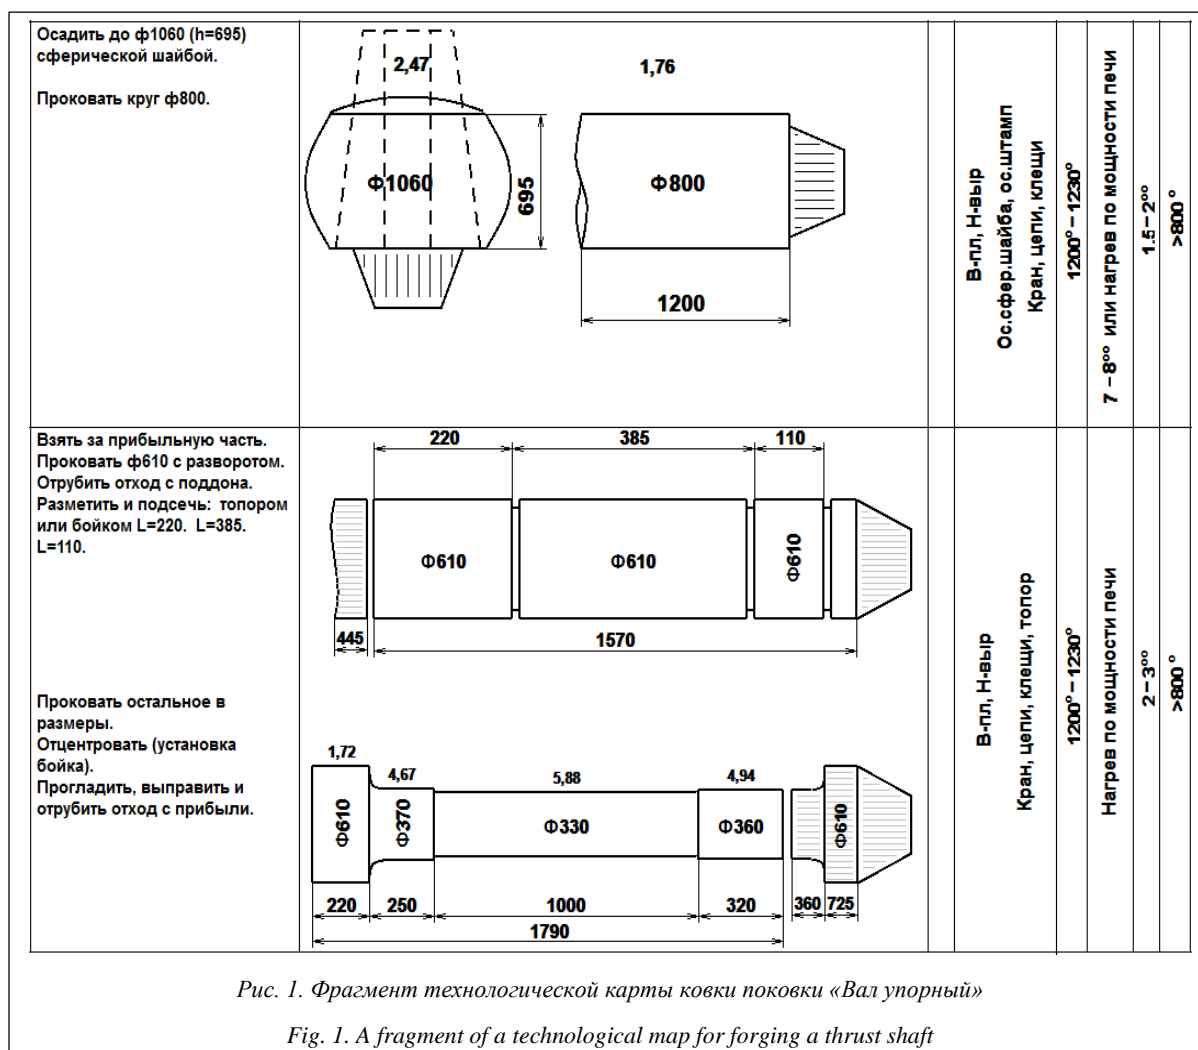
Фрагмент технологической картыковки поковки «Вал упорный»
